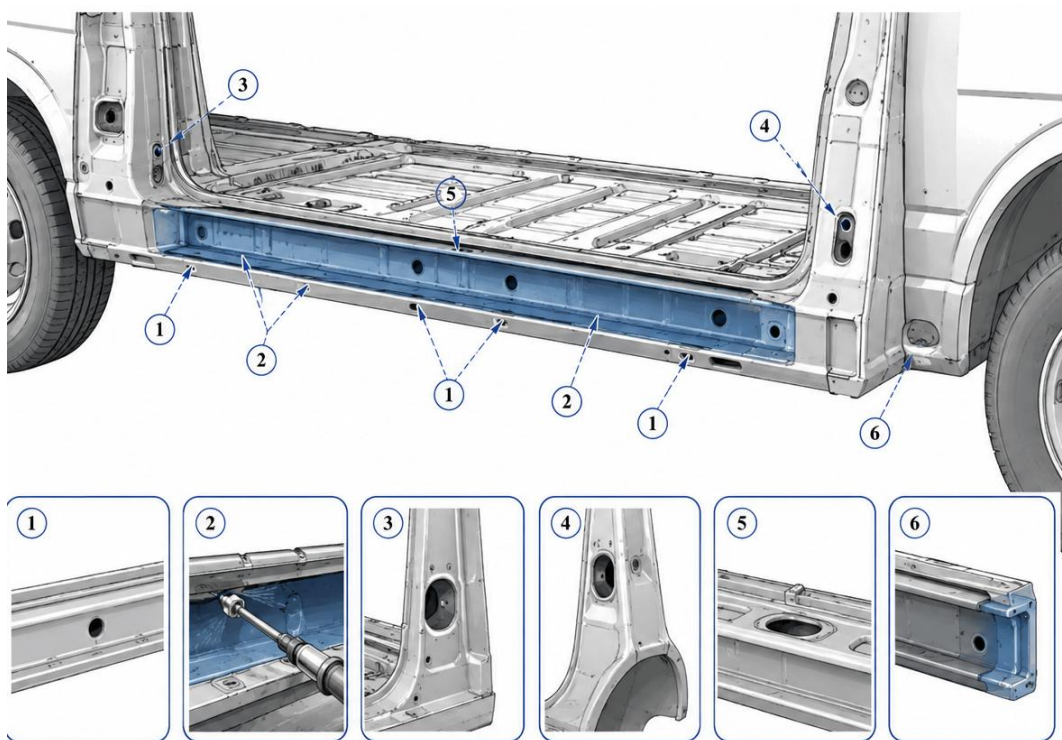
Контроль антикорозійної обробки внутрішньої порожнини порога:
